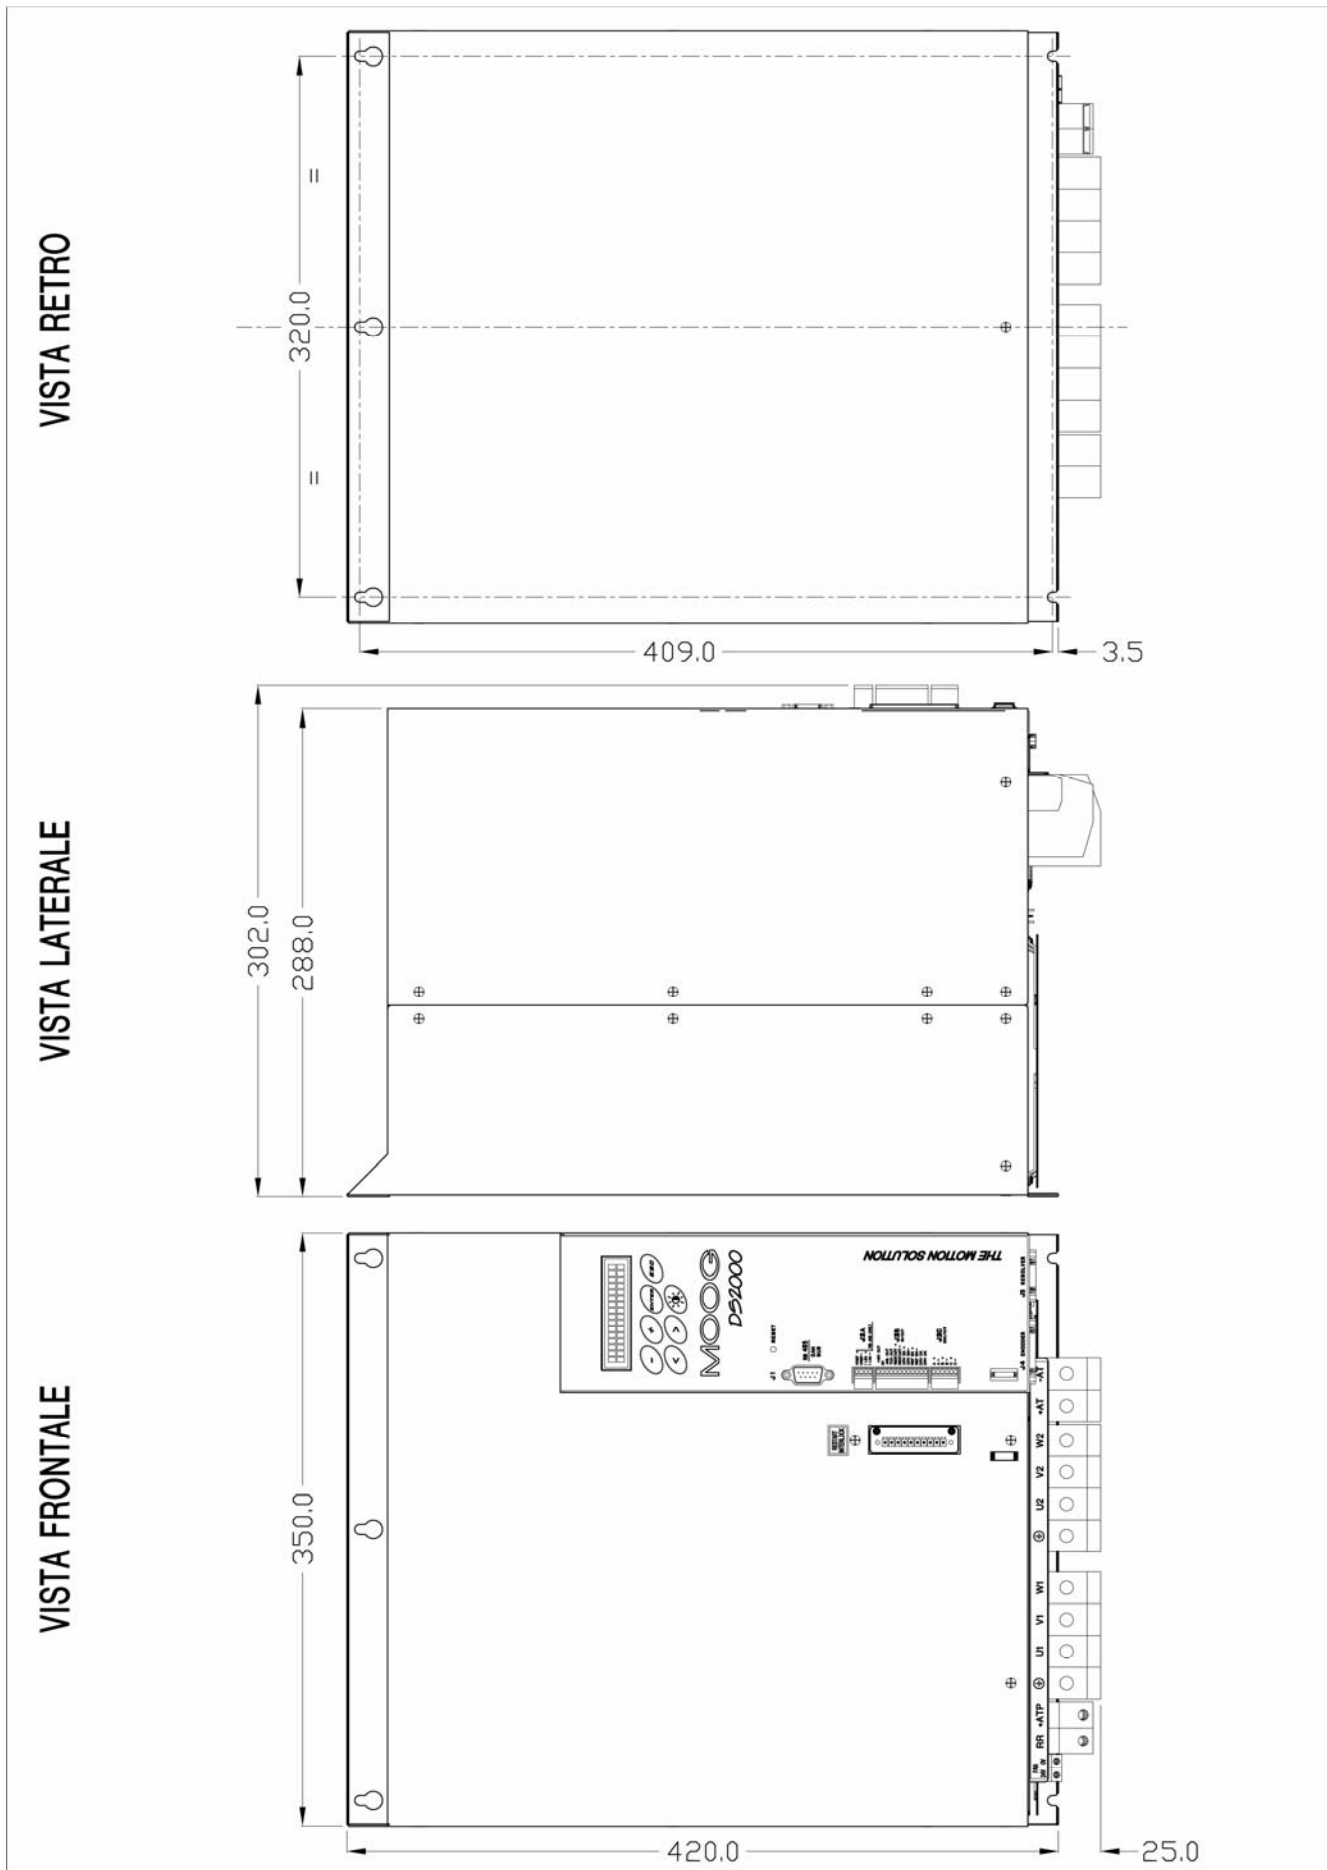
Dimensioni e fissaggi (mm) taglia E
